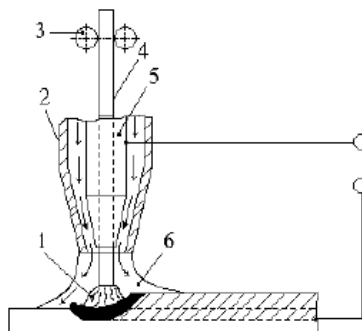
Дуговая сварка в защитном газе плавящимся электродом: 1 – электрическая дуга; 2 – газовое сопло; 3 – подающие ролики; 4 – электродная проволока; 5 – токоподводящий мундштук; 6 – защитный газ
